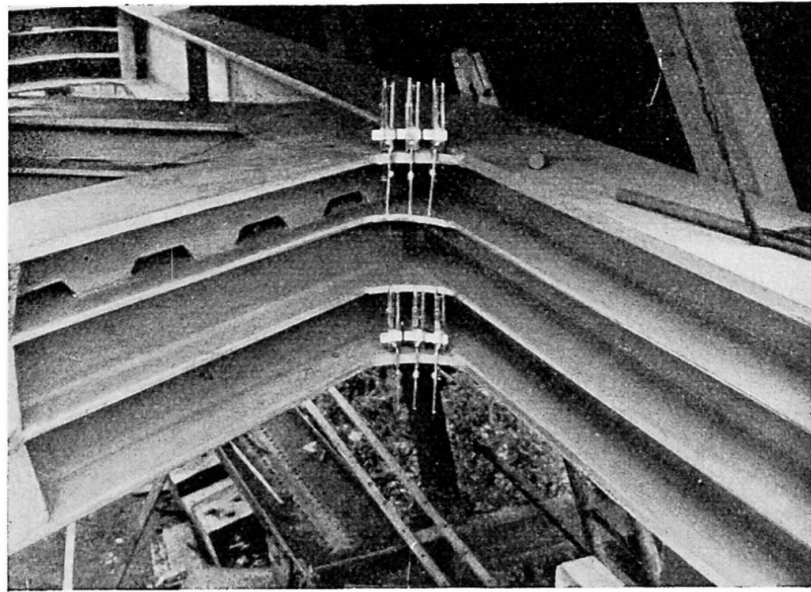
Soudure en atelier d'une poutre fixée sur ses roues d'orientation.
